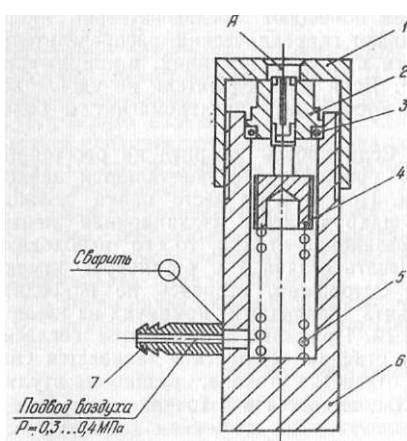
Устройство для проверки клапанной пары на герметичность:
